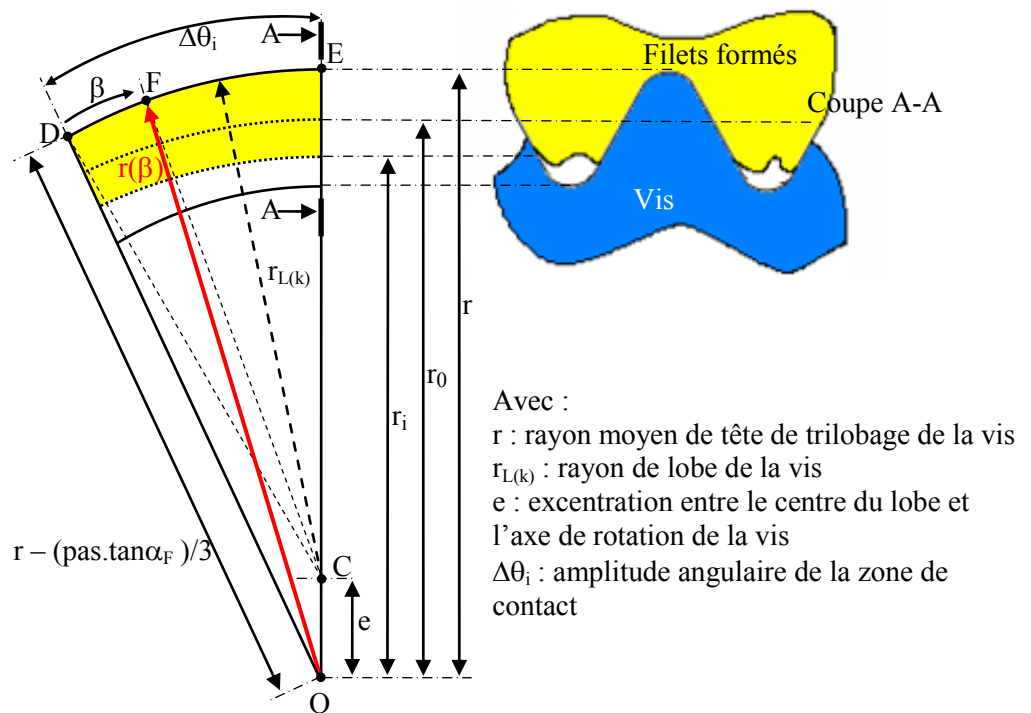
Surface en contact du dernier lobe qui forme les filets et définition des paramètres géométriques.
